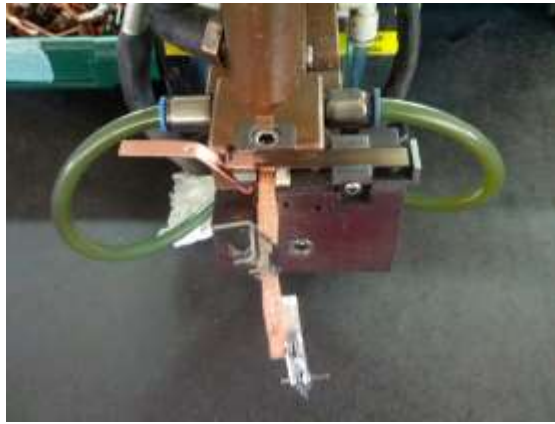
Jig destinado á operação de soldadura trança/pista de arco e pista de arco/bimetal
